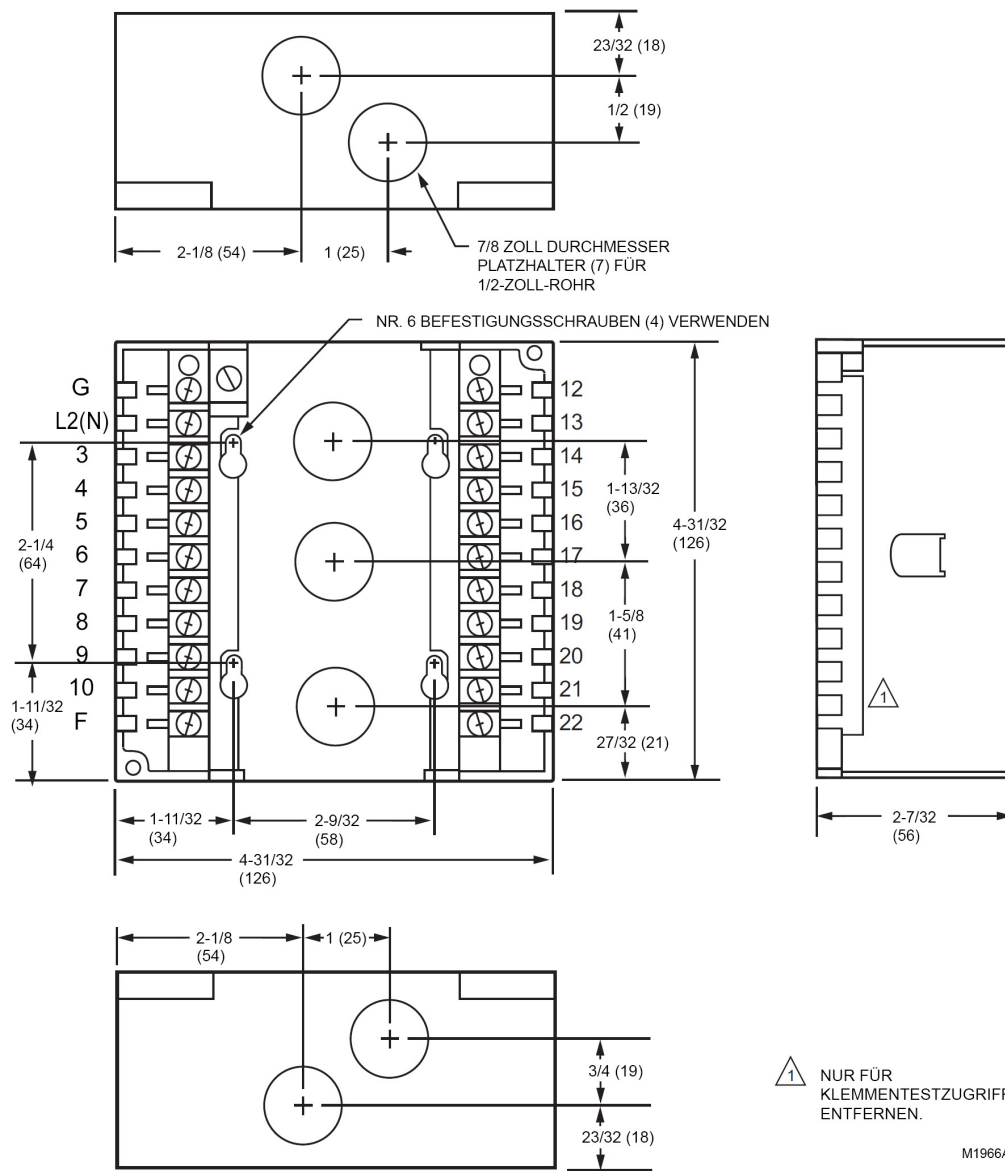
Draufsicht und Frontansicht des Q7800B1003-Verdrahtungssockels (4-seitig) mit Abmessungen in Zoll (mm).
